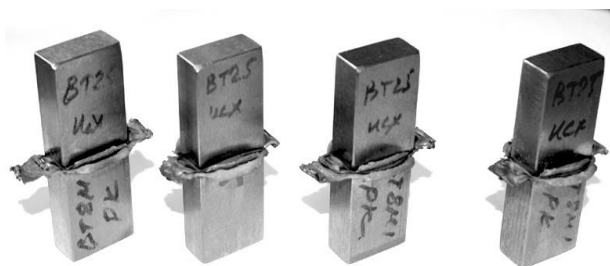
Сваренные образцы сплавов BT8M-1 и BT25U между собой
